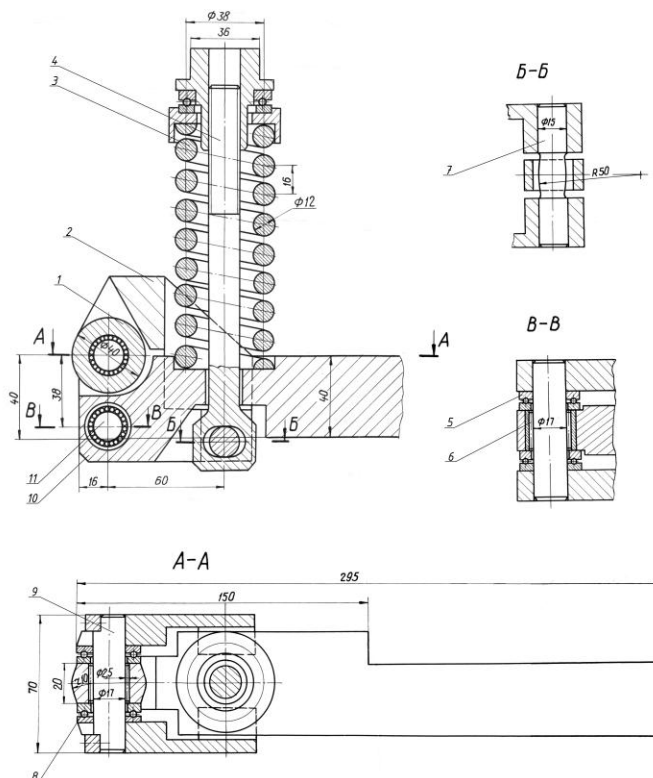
Устройство для обкатывания деталей торообразным роликом со стабилизацией усилия обкатывания
